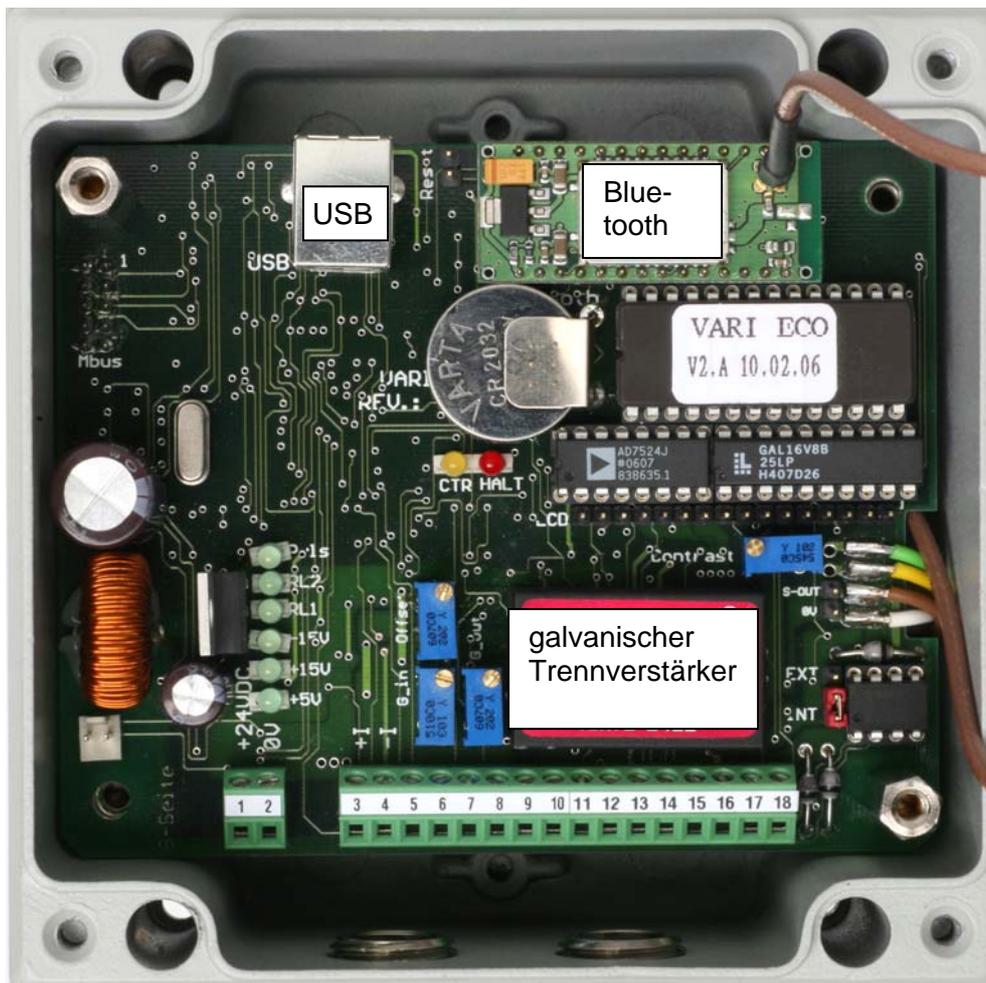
ECO Elektronikplatine mit Optionen Bluetooth, galvanischer Trennung & USB
